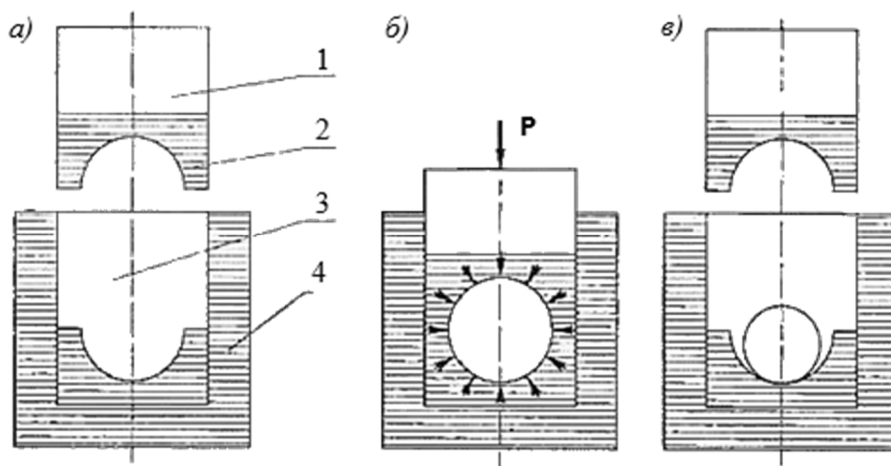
Схема квазіізостатичного пресування сферичної заготовки:
